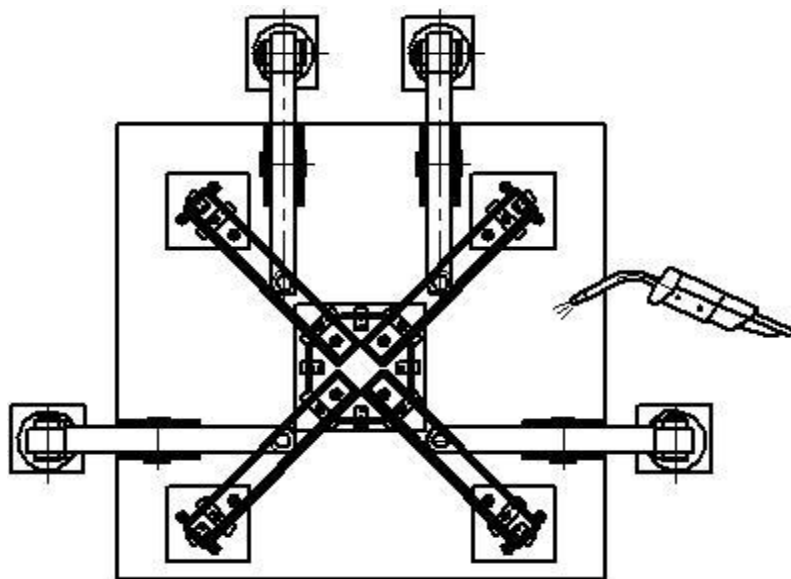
Условная схема выполнения технологических операций «сборка» и «сварка» для раскосой решётки
